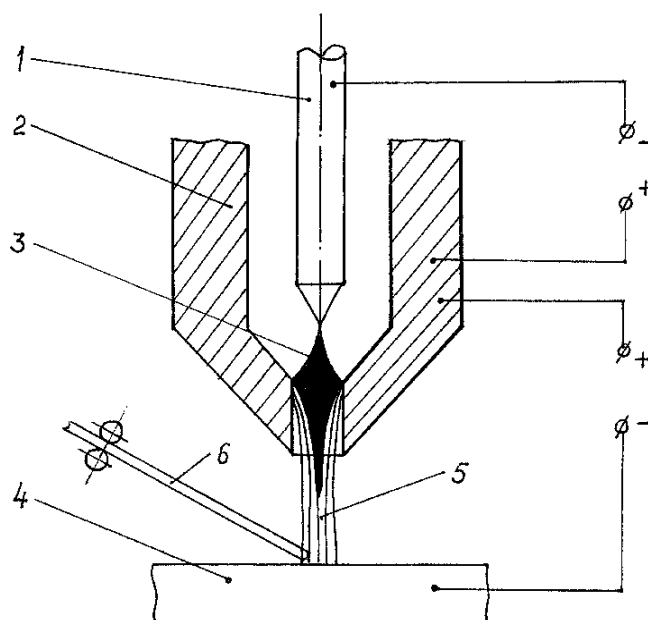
Схема плазменной сварки с полым анодом алюминиевых сплавов:
